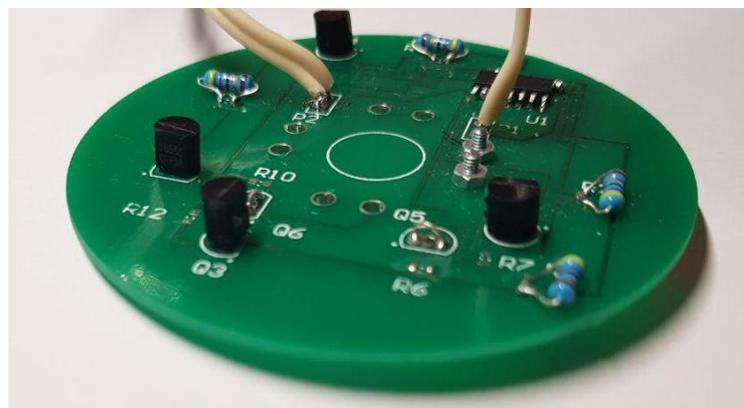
Placa de circuito impreso en proceso de soldadura
